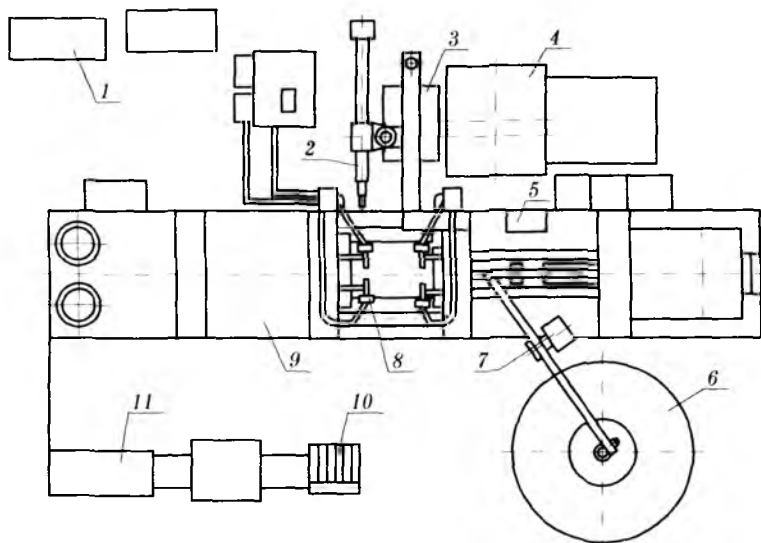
Схема автоматической линии изготовления отливок литьём под давлением (вид сверху):
